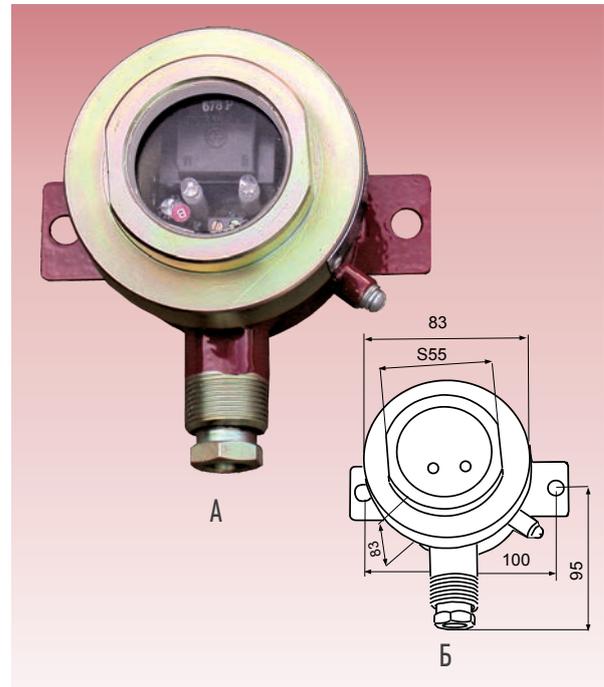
Сигнализатор ВУУК-МС-КС: А - внешний вид, Б - габаритные и установочные размеры.
